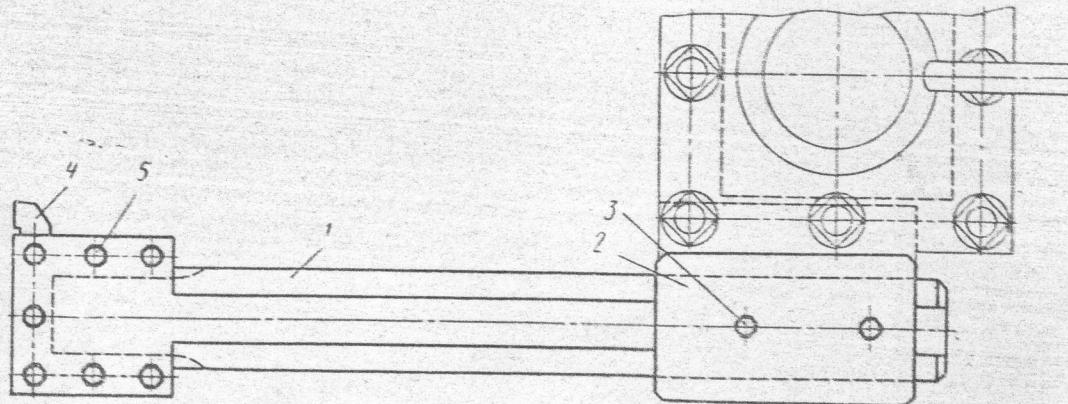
Резцовая оправка для обработки деталей над выемкой в станине
